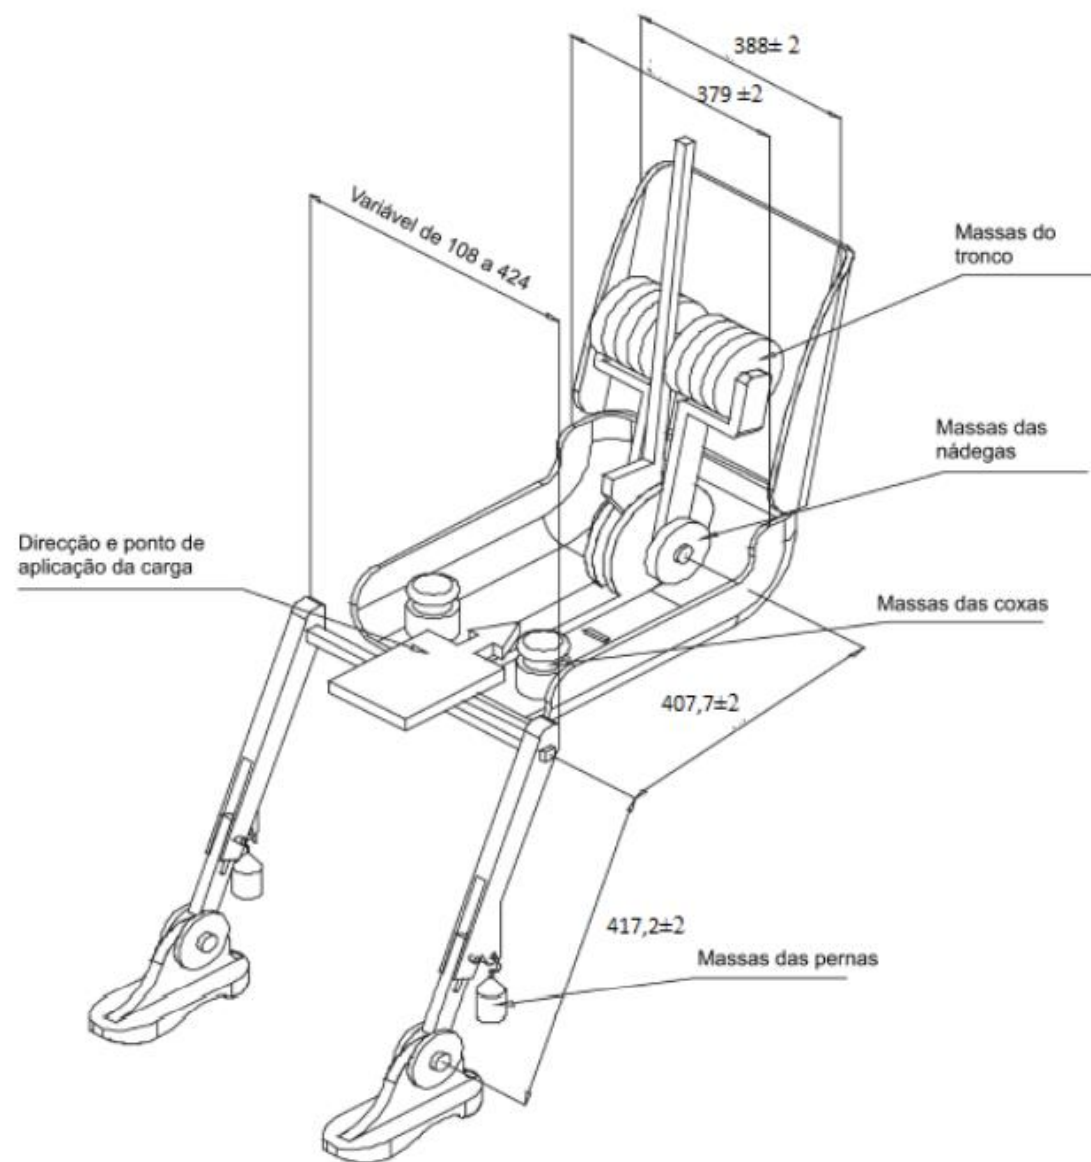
Dimensões dos elementos da máquina 3-D H e distribuição de peso (dimensões em milímetros)
